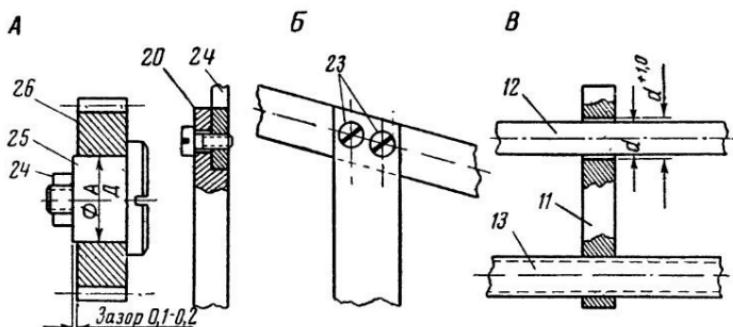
Модель механизма подачи суппорта токарного станка (схема соединения деталей): А — крепление зубчатого колеса «трензеля» (24 — планка, 25 — ось зубчатого колеса, 26 — зубчатое колесо); Б — соединение планок (20, 24 — планки, 23 — винты); В — узел «суппорта» (11 — «суппорт», 12 — направляющая «суппорта», 13 — «ходовой винт»).
